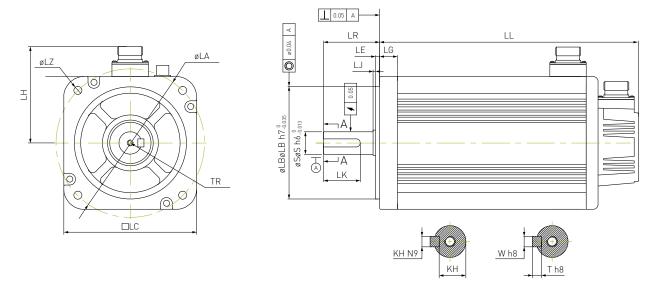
Габаритные размеры серводвигателя ELM2M-xxx (220VAC).
